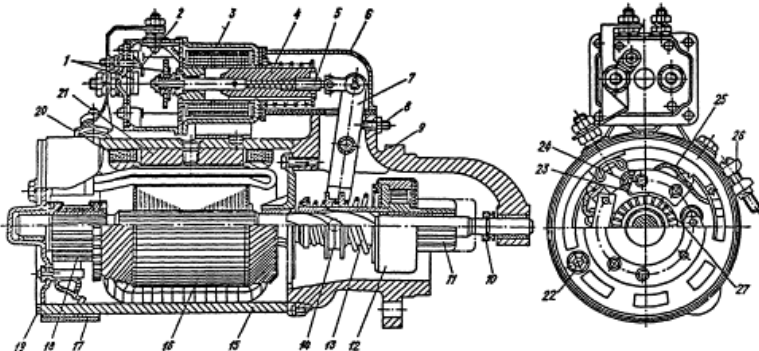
Будова стартера: 1 - контакти тягового реле; 2 - контакти замикання додаткового резистора котушки запалювання; 3 - обмотки тягового реле; 4 - якір тягового реле; 5 - регулювальний гвинт-тяги; 6 - захисний кожух важеля; 7 - важіль; 8 - гвинт регулювання ходу шестірни; 9 - кришка з боку приводу; 10 - упорне кільце; 11 - шестерня приводу; 12 - муфта вільного ходу; 13 - пружина; 14 - повідкова муфта; 15 - корпус; 16 - якір; 17 - захисна стрічка; 18 - колектор; 19 - кришка з боку колектора; 20 - обмотка збудження; 21 - полюс; 22 - стяжна шпилька; 23 - щіткотримач; 24 - пружина щіткотримач; 26 - стяжний гвинт захисної стрічки; 27 — щітка.
